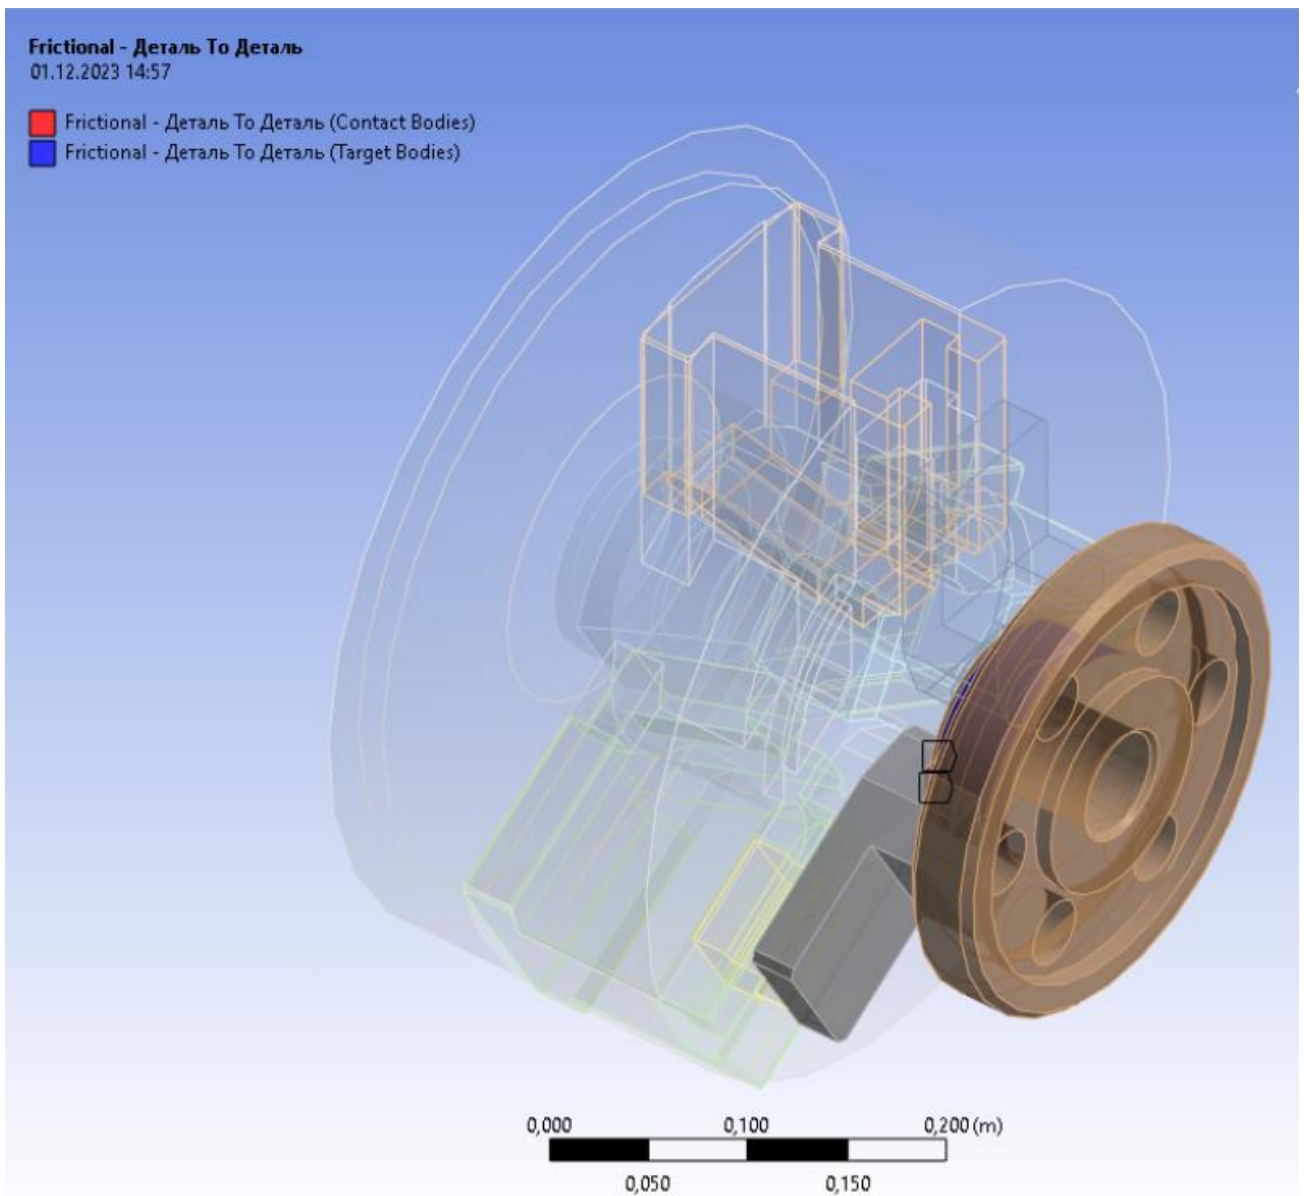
Сполучення поверхні змінного кулачка та зовнішньої циліндричної поверхні деталі
